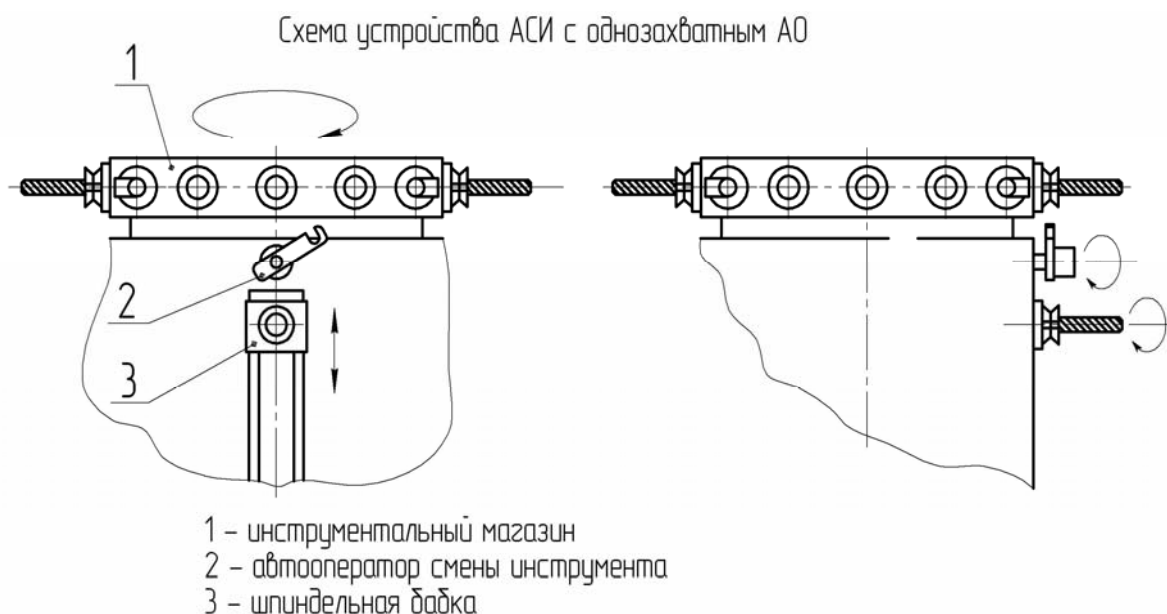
а – Схема устройств АСИ с однозахватным автооператором
